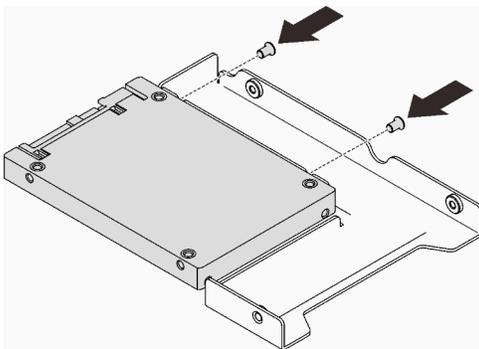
Anbringen der Schrauben, um das Laufwerk am Laufwerkadapter zu befestigen
